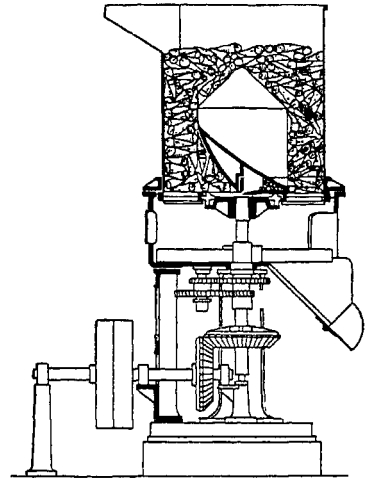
Schnitt durch die Rübenschnitzmaschine von SELWIG & LANGE, Braunschweig.
